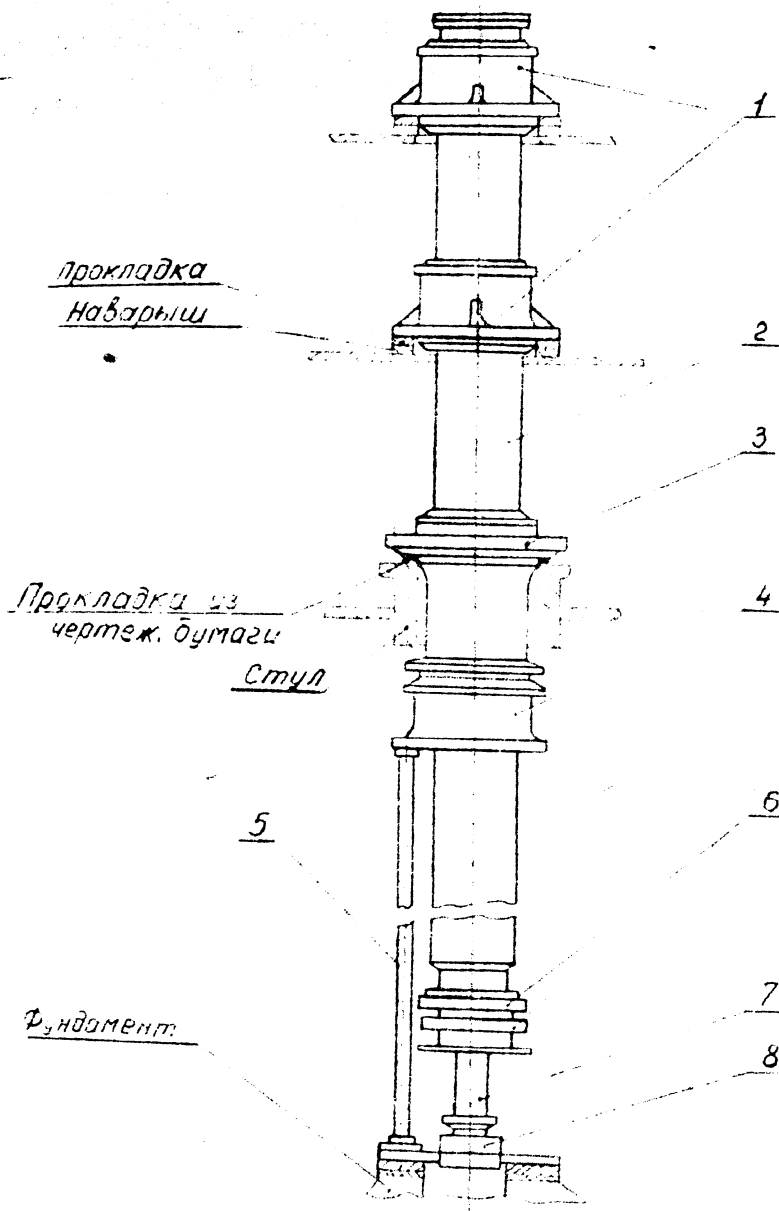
Схема конструкции подземно-мачтового устройства неагрегатного исполнения
